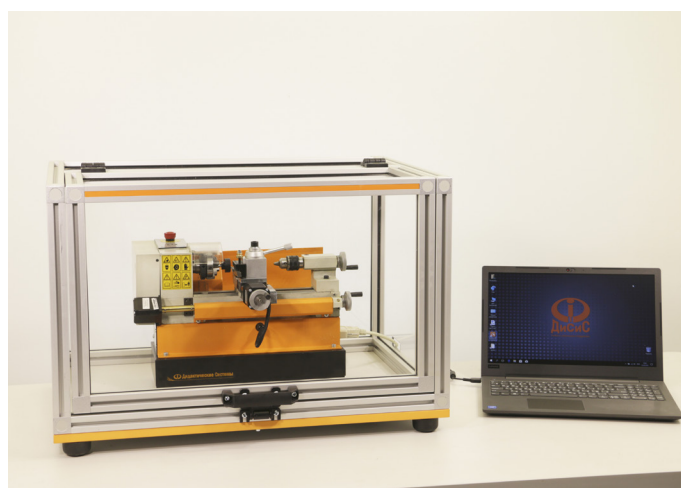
Настольный токарный станок «Юниор-Токарный»
